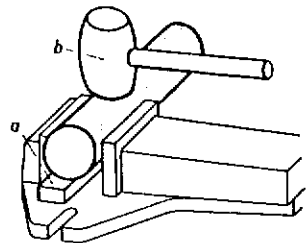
(izquierda). Colocación del eje utilizando el mazo de madera. a) Pieza paralelepípedica; b) mazo de madera.
